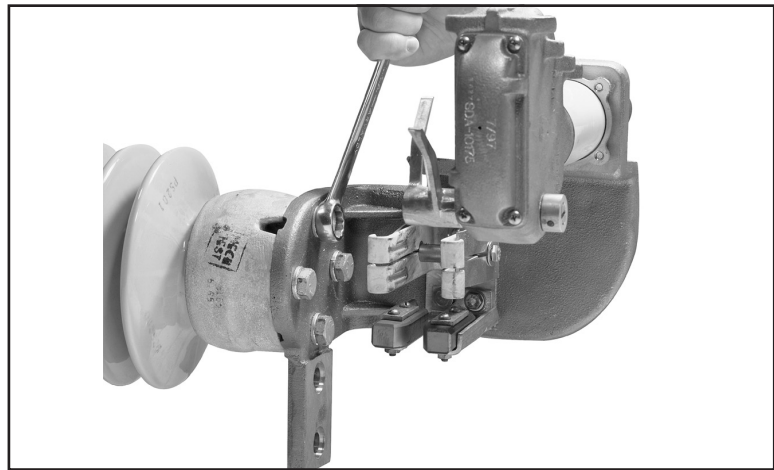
Colocando la pieza fundida de reemplazo de la base terminal con calzadores instalados.
